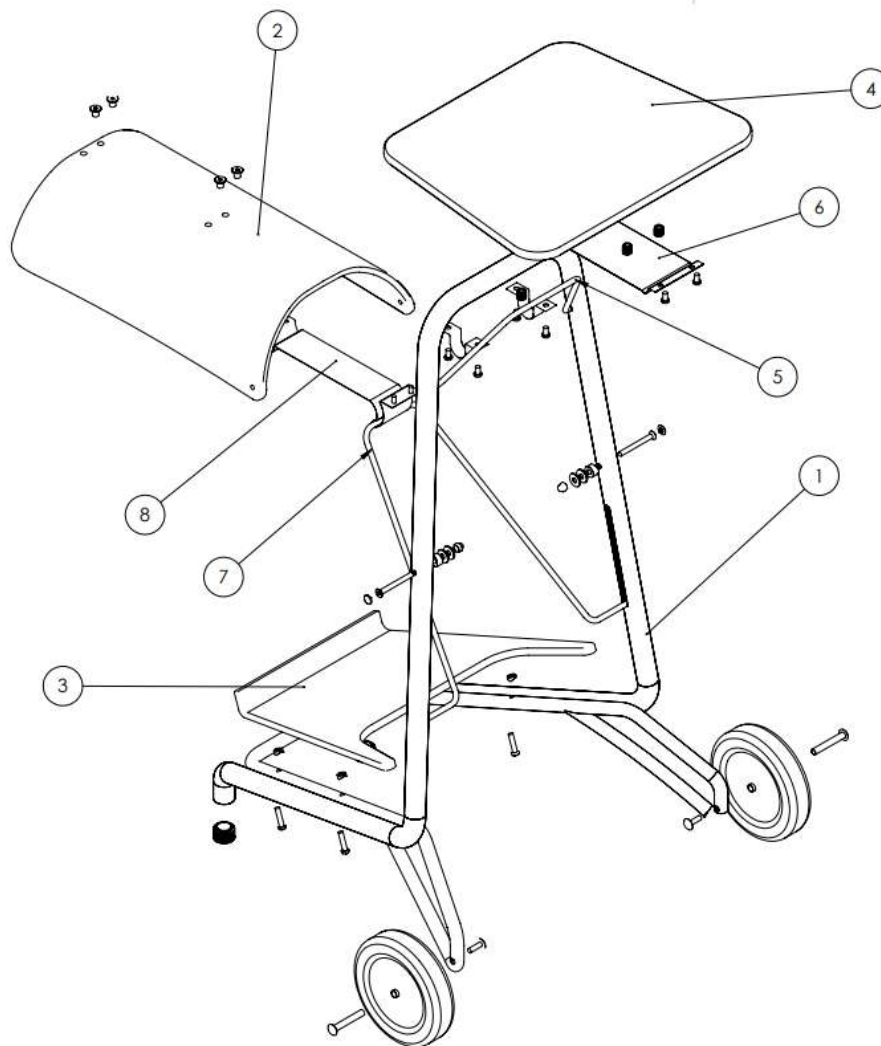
Explosionado con las piezas diseñadas. Fuente: Elaboración propia (2023)
